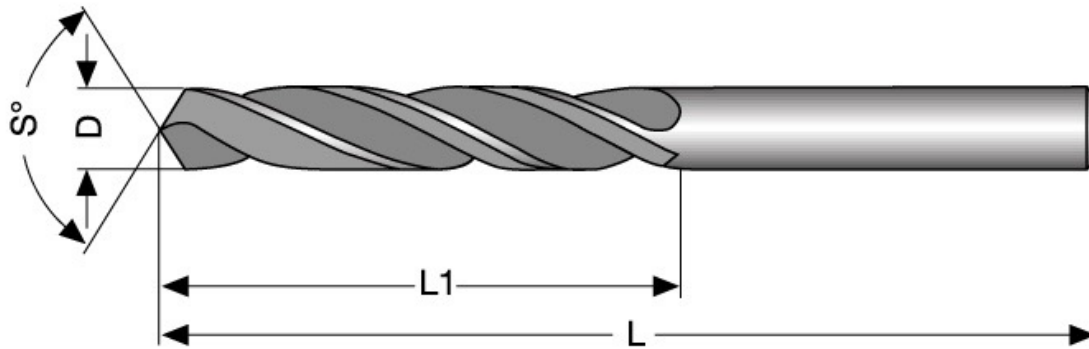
Bildmaterial von Spiralbohrer, Quelle: Internet
